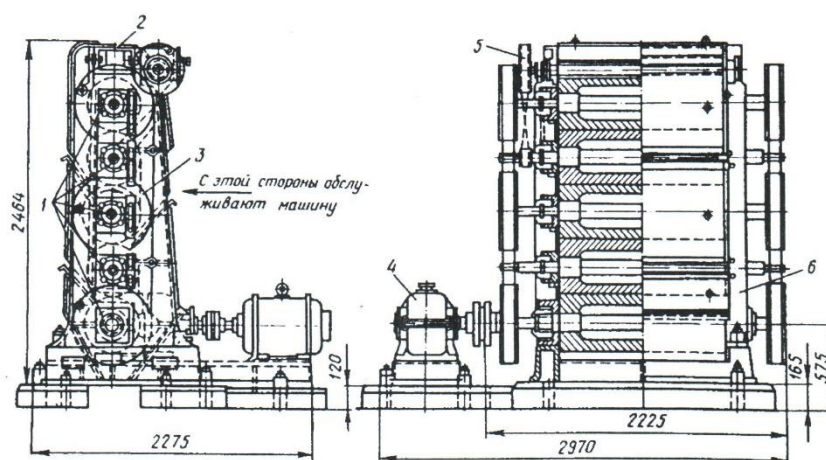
Схема п'ятивальцевого станка ВС-5
